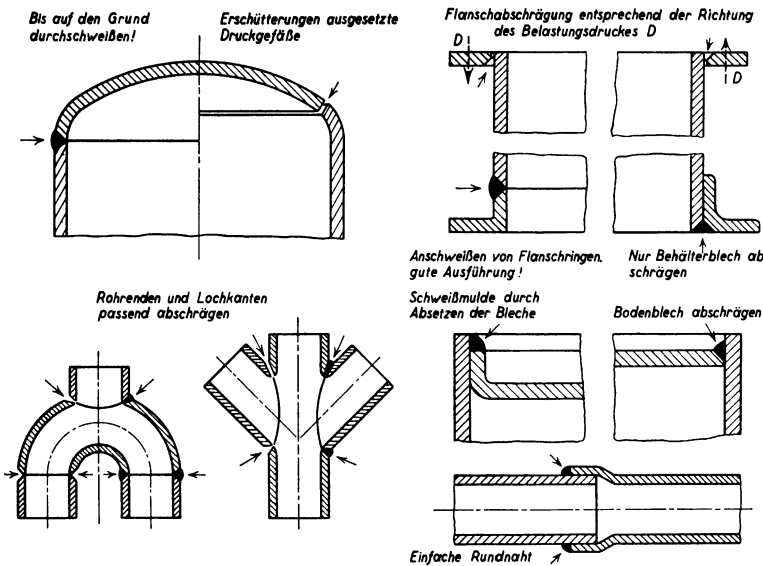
Rohrverbindungen durch Schweißen.
